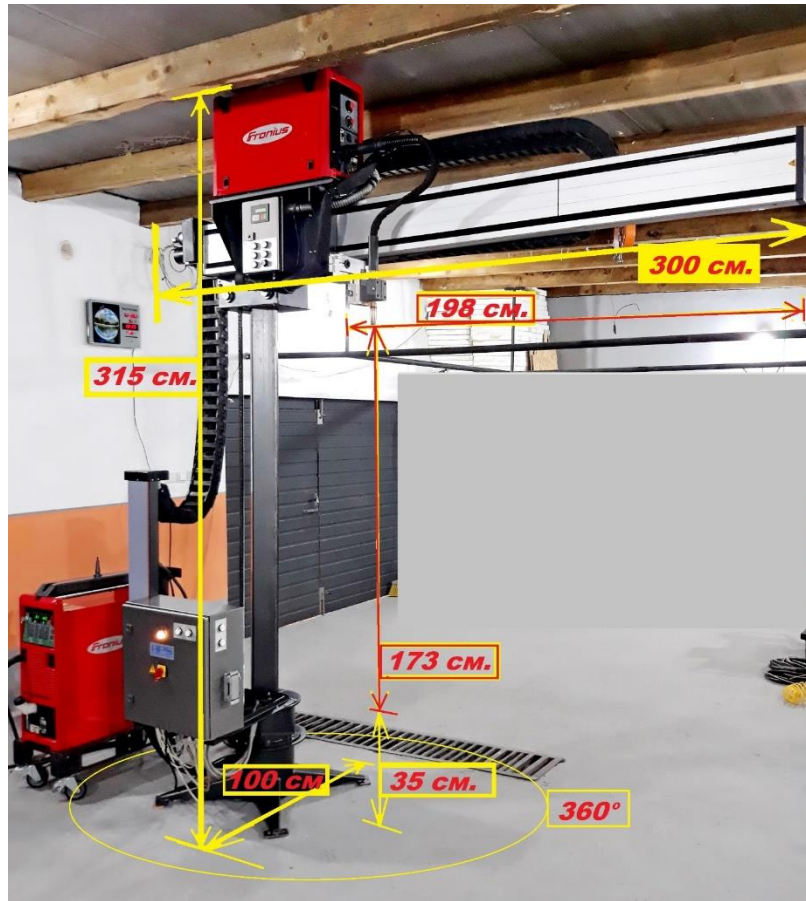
Зварювальна колона для автоматичного зварювання
